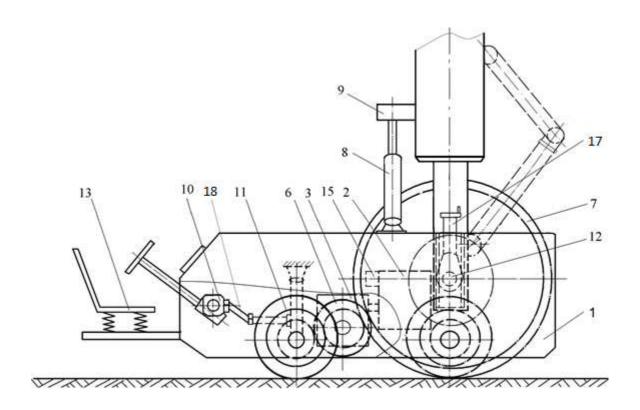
Малогабаритное буксировочное устройство: 1 — несущая рама; 2 — двигатель (силовой агрегат); 3 — редуктор; 6 — ведущий ролик привода колес воздушного судна; 7 — колесо воздушного судна; 8 — механизм догрузки; 9 — упор передней стойки самолета; 10 — рулевой механизм; 11 — управляемые ведущие колеса буксировочной тележки; 12 — механизм фиксации буксировочной тележки к передней стойке шасси воздушного судна; 13 — сидение водителя; 15 — гидравлический насос с распределителем; 17 — винт; 18 — рулевая тяга
